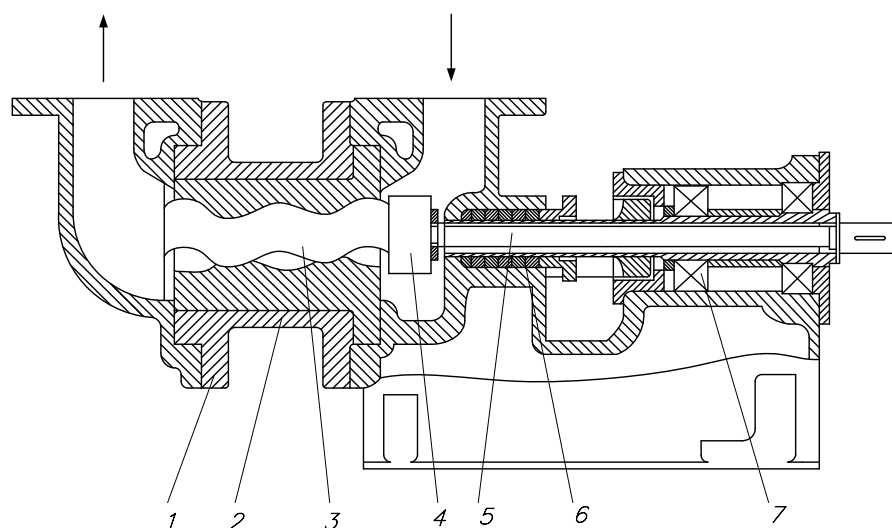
Одновинтовой насос: 1 – корпус; 2 – обойма; 3 – винт; 4 – муфта; 5 – вал; 6 – уплотнение; 7 – опора с подшипниками
